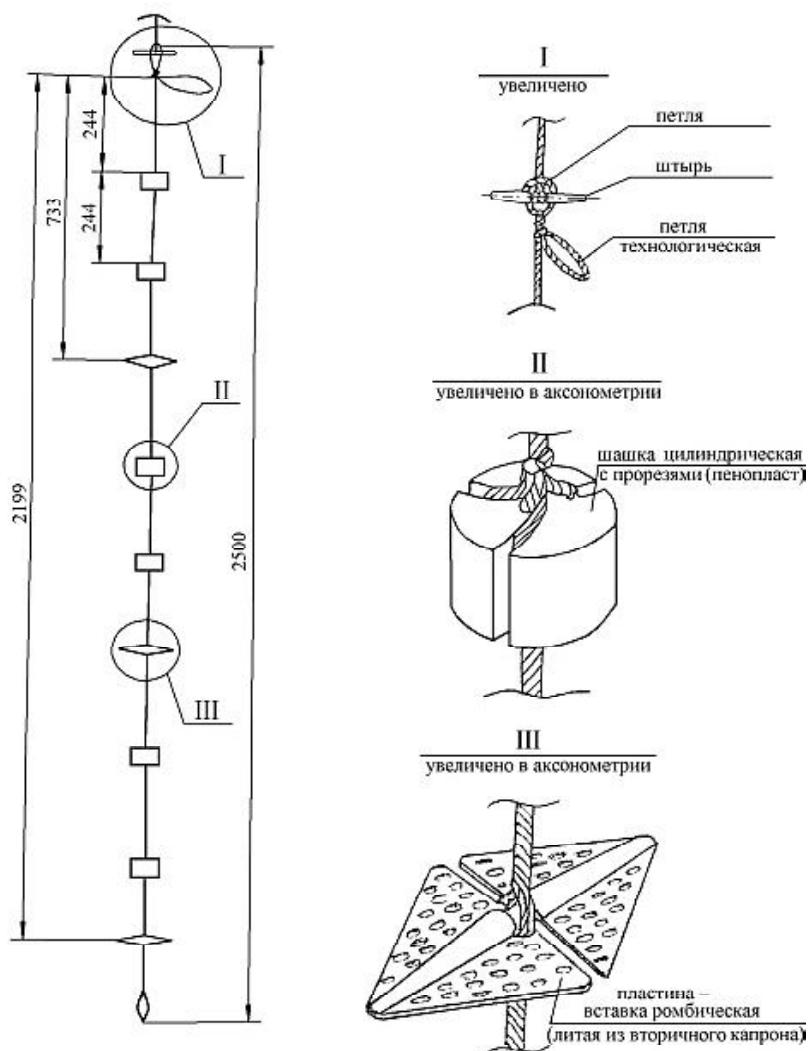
Коллектор «непрерывнопроцессного» типа для сбора личинок и выращивания товарных мидий
